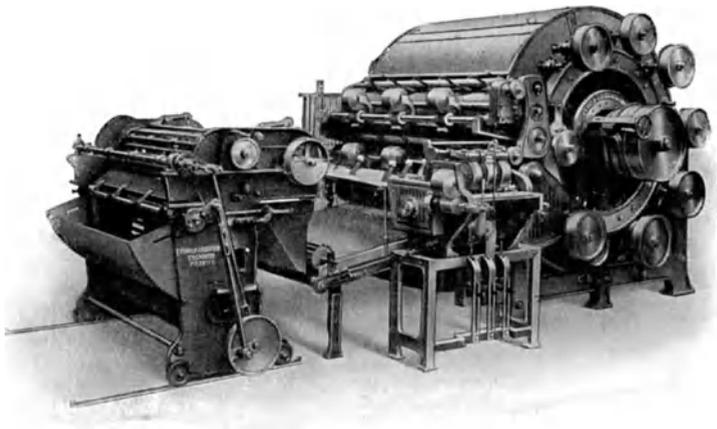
Hanfwerk-Feinkarde mit Auflegemaschine.
